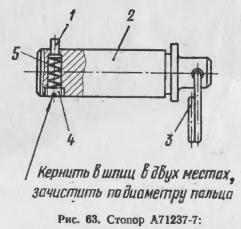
Стопор А71237-7: 1— стопор А51620-47; 2— палец А51621-50; 3— кольцо А51203-175; 4— пробка А52150-12; 5— пружина А51230-109
